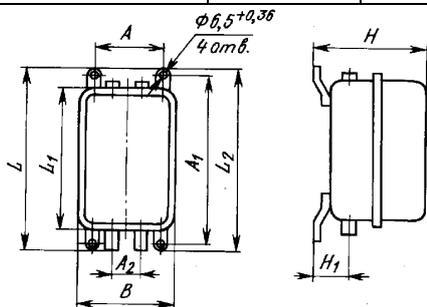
Габаритные, установочные размеры пускателей нереверсивных типов ПМ12-080, ПМ12-100, ПМ12-160 степени защиты IP54
